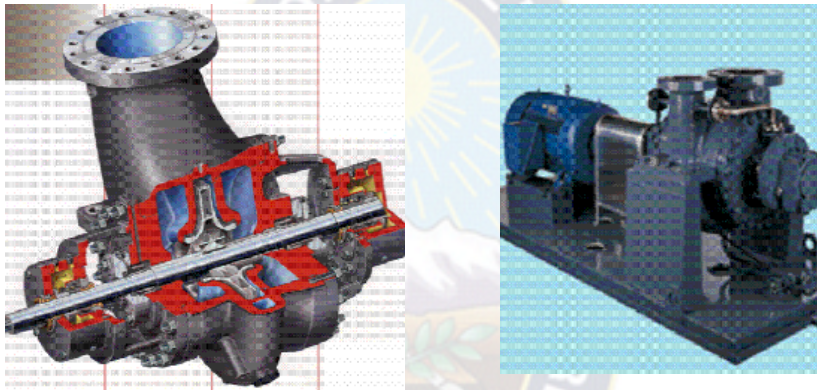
Bomba Unietapa de doble succiones radialmente partida, impulsor entre cojinetes.
